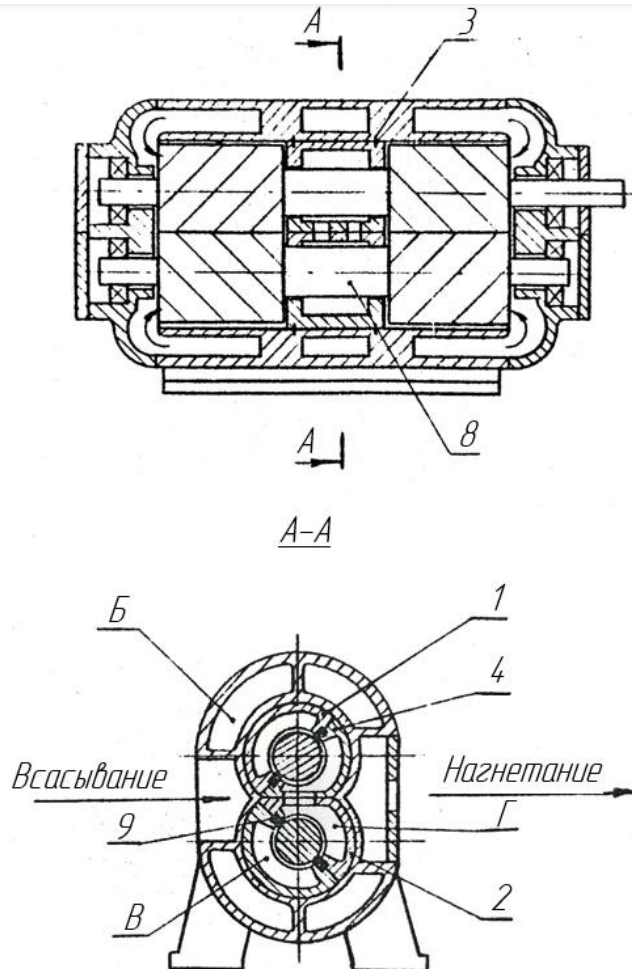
Одноступенчатый винтовой компрессор с шевронной схемой роторов
